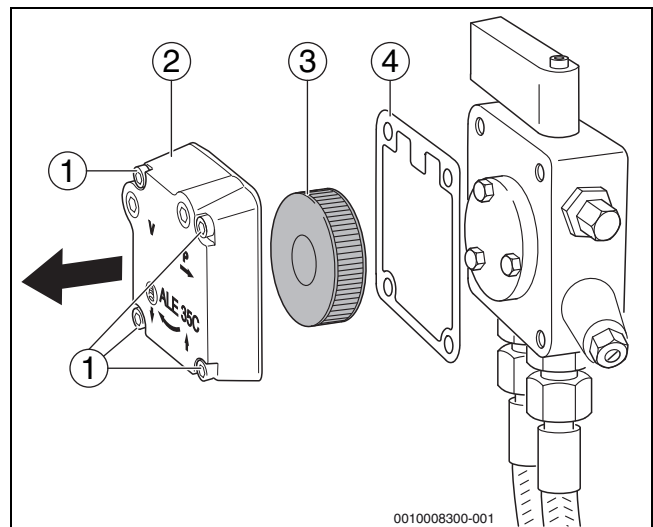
Contrôler le filtre de la pompe à fioul – Pompe à fioul Suntec
